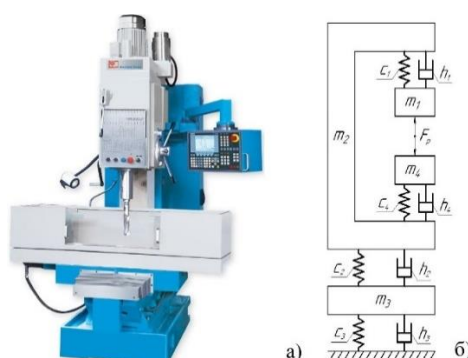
Вертикальный сверлильный станок KSB 40 CNC: внешний вид станка (а),
